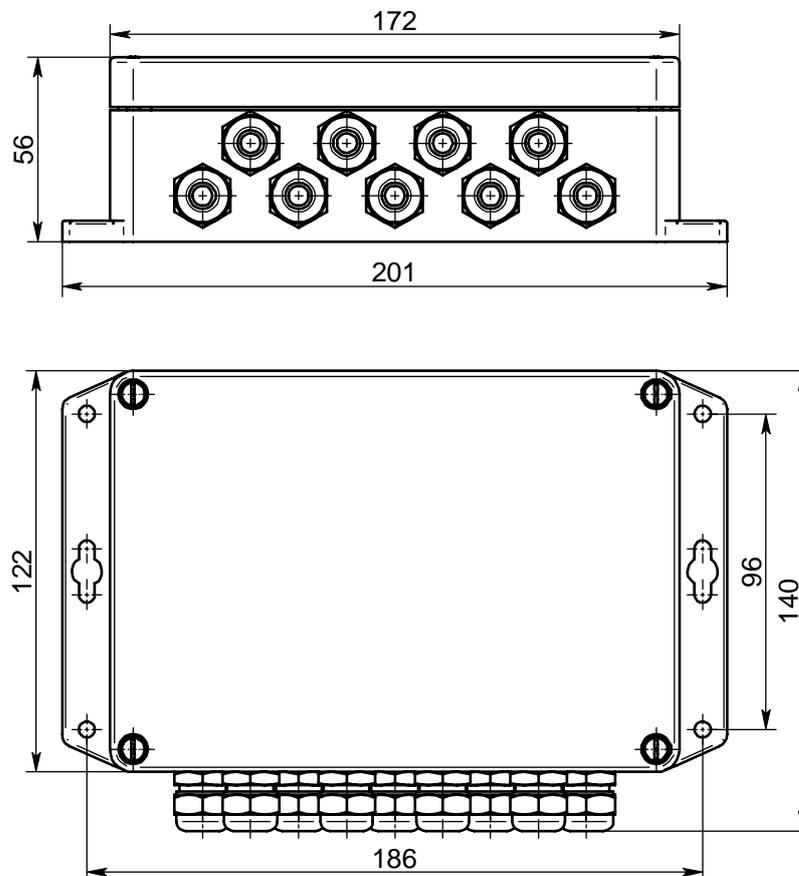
Габаритные и установочные размеры вторичных преобразователей ВП-XXX-X-X-НА... и ВП-XXX-X-X-НП
